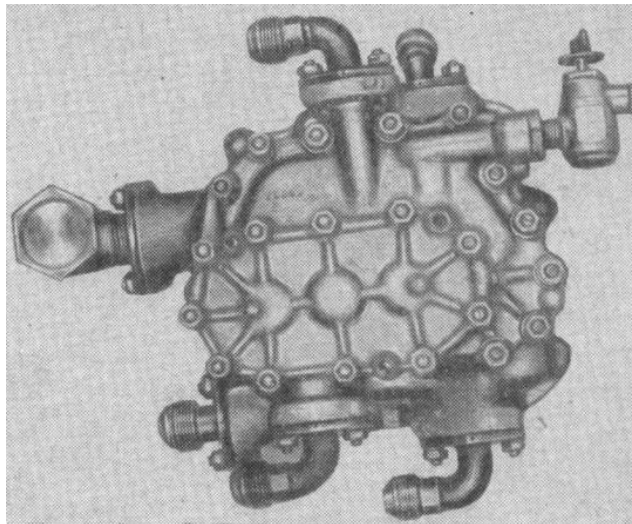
Нижний масляный агрегат (вид снизу)
